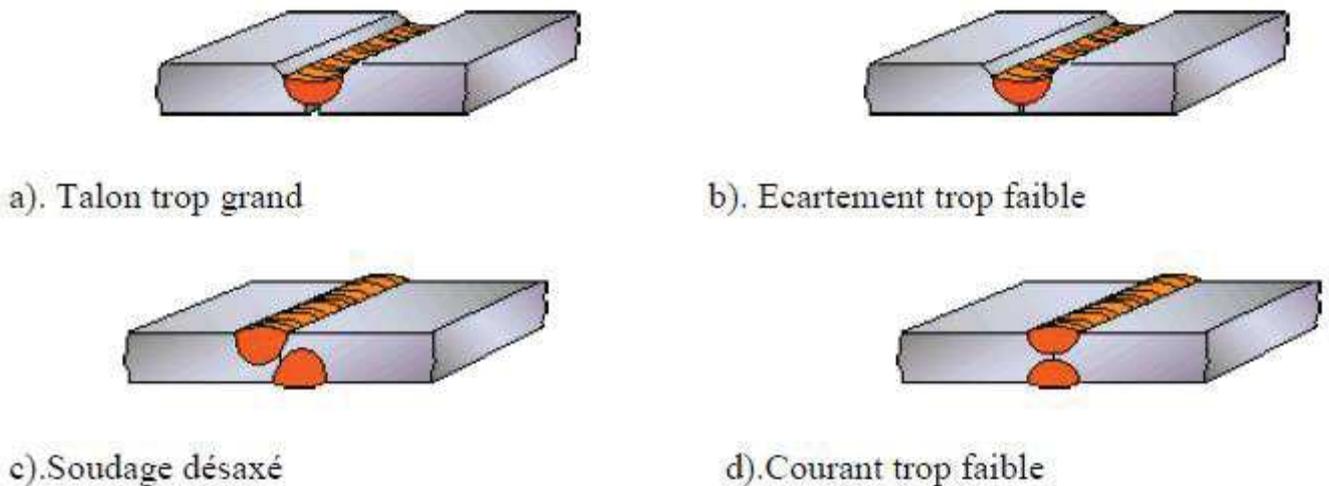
Manque de pénétration dans la soudure.
